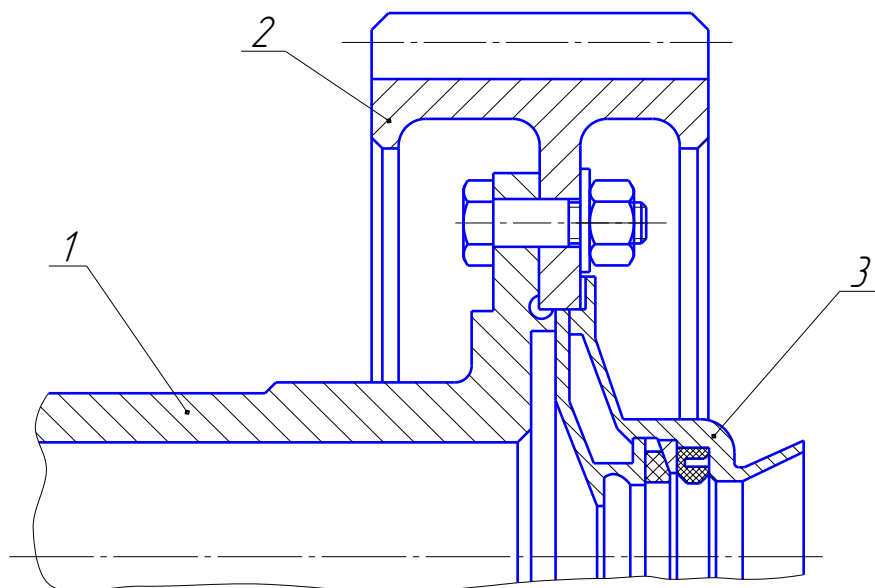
Соединение ведомого колеса редуктора ВР-2Б с валом несущего винта.
